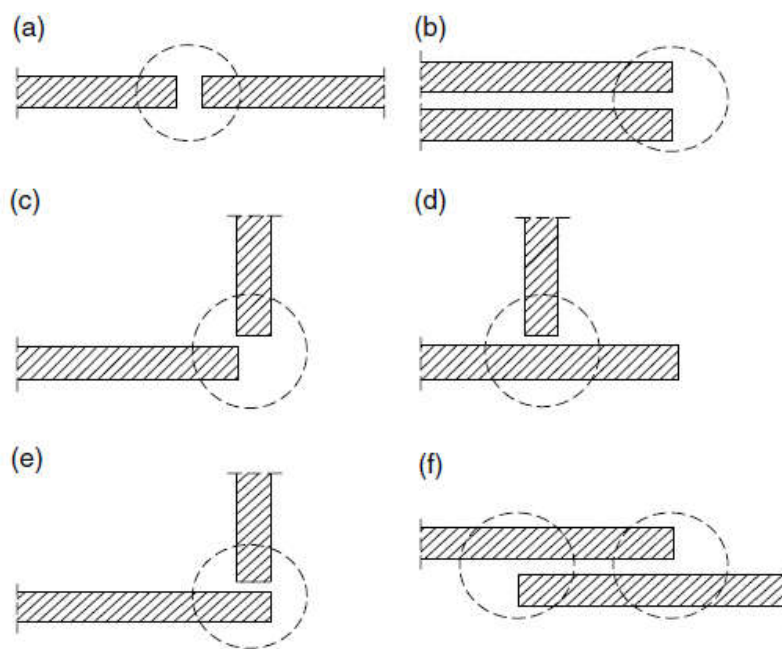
Classification basée sur la position relative des éléments à assembler : (a) joint bout à bout, (b) joint de bord, (c) joint d'angle, (d) joint en T, (e) joint en L et (f) joint à recouvrement
